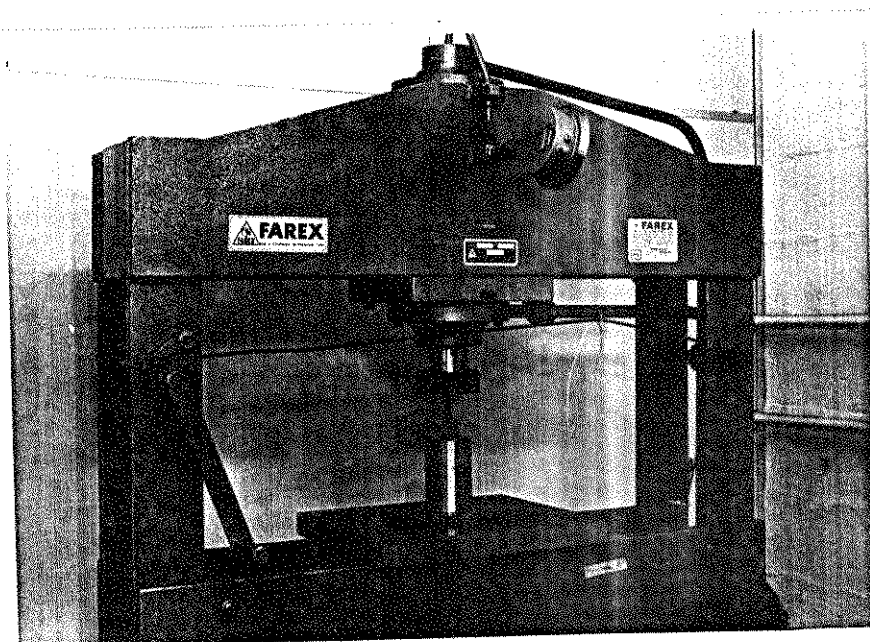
Vista da prensa com o sistema de extrusão devidamente montado.
